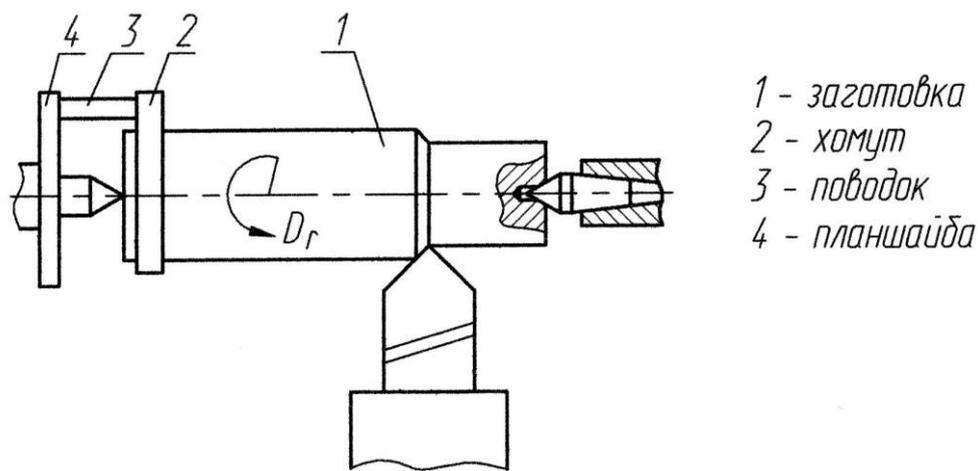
Установка заготовки в центрах и поводковом патроне
